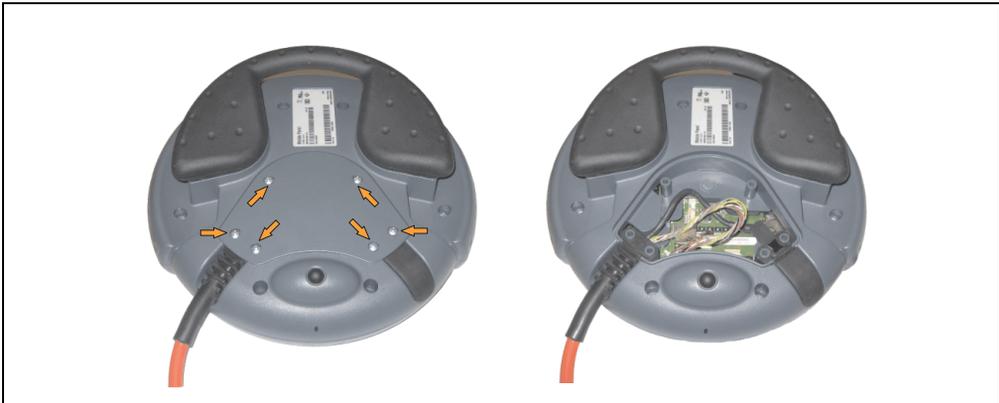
Abdeckung des Anschlusschachtes entfernen
